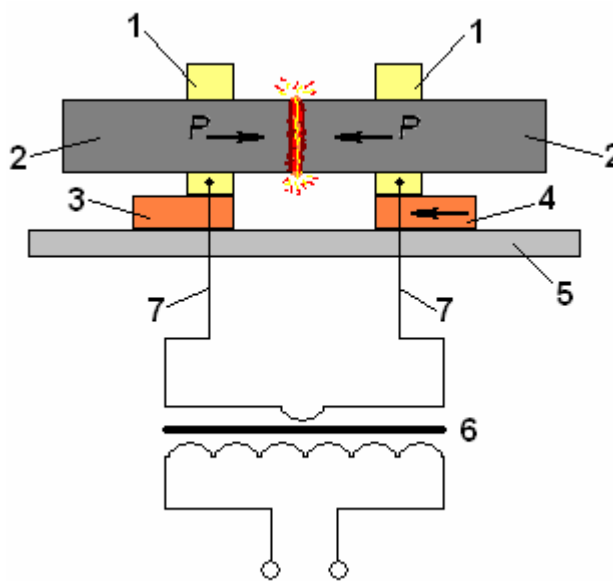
Схема стыковой электроконтактной сварки
